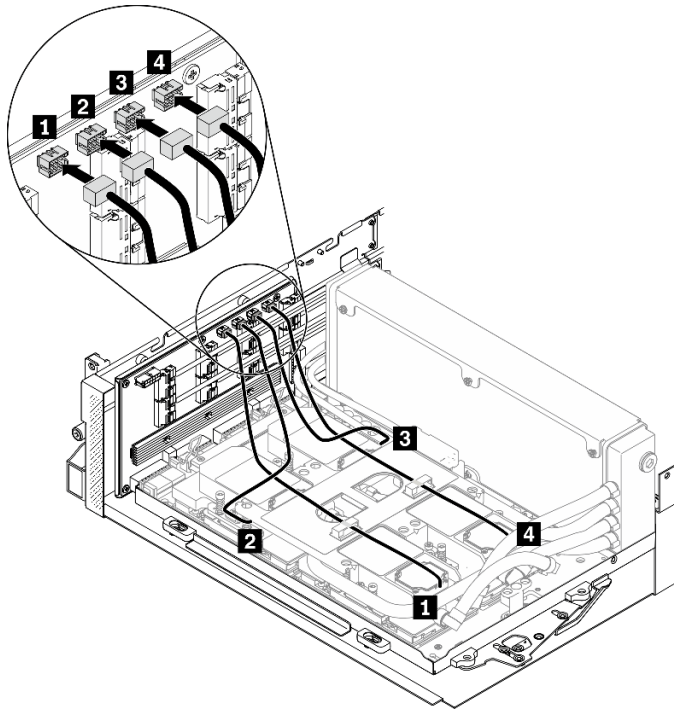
Disposición de los cables de la bomba del conjunto de placa de frío al conjunto de retemporizador: Configuración G
